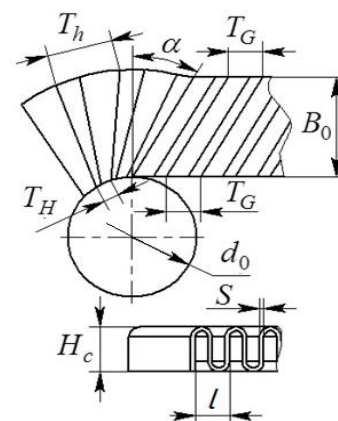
Розрахункова схема навивання гофрованої заготовки на оправу
